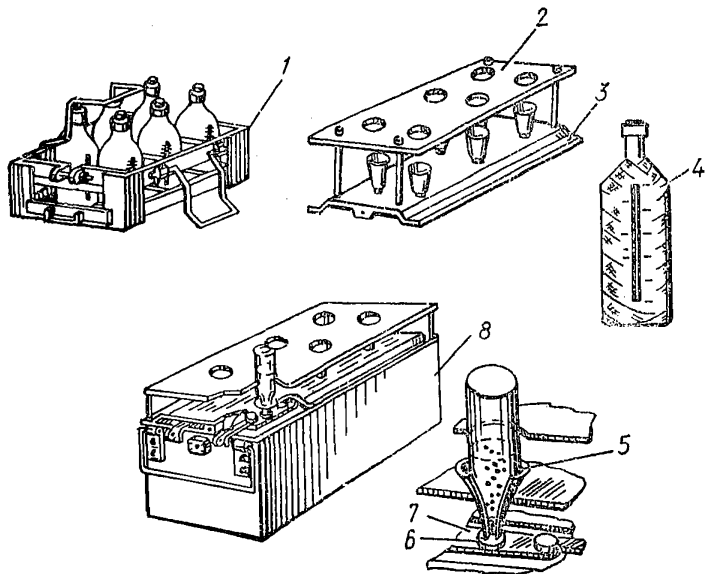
Приспособление для заливки аккумуляторных батарей:
